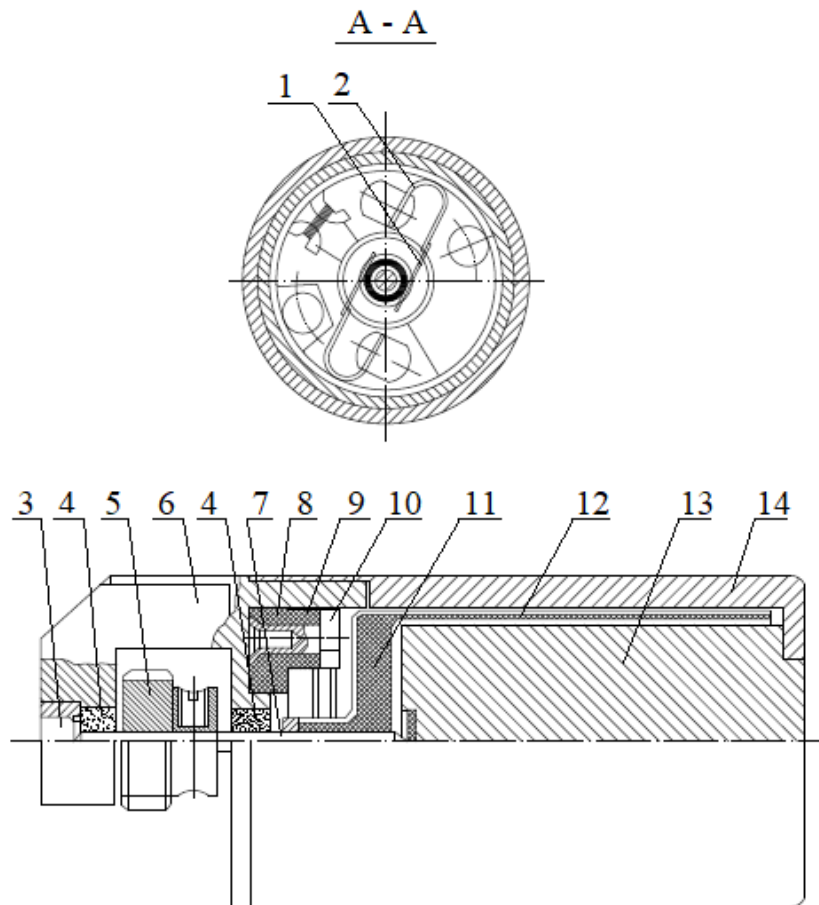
Загальний вигляд електродвигуна: 1-щітка, 2-пластина, 3-гвинт, 4-підшипник, 5-трібка, 6-кронштейн щіткотримача, 7-вал, 8-плата щіткотримача, 9-стійка, 10-основа щіткотримача, 11-ламелль колектора, 12-обмотка якоря, 13-магніт, 14-корпус (магнітопровід)
